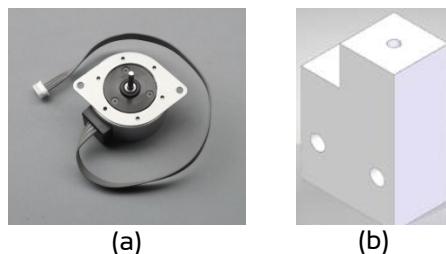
a) Motor paso a paso, b) Pieza para unir la sonda de voltaje al eje del motor [fuente propia]
